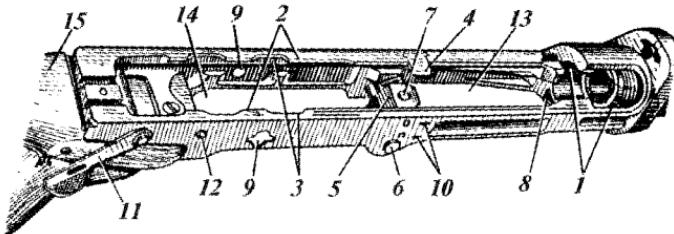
Ствольная коробка СВД-63: 1 — вырезы для запирания затвора; 2 — отгибы; 3 — вырезы в отгибаах; 4 — отражательный выступ; 5 — перемычка; 6 — ось перемычки; 7—останов затвора; 8—вырез для зацепа магазина; 9—отверстия для предохранителя; 10—фикссирующие выемки; 11 — замыкатель крышки ствольной коробки; 12 — фиксатор замыкателя; 13 — окно для магазина; 14 — окно для ударно-спускового механизма; 15 — приклад.
